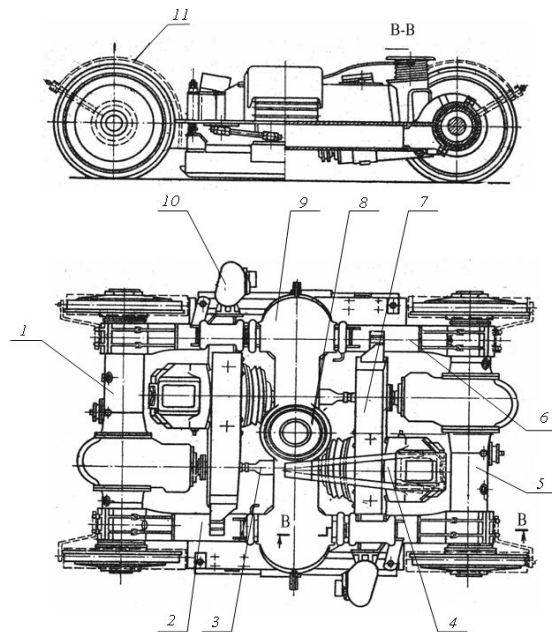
Візок вагона Т-3: 1, 5 – колісні пари, 2, 6 – поздовжні балки, 3 – карданний вал, 4 – тяговий двигун, 7 – балка для підвішування тягового двигуна, 8 – пятник, 9 – люлька візка, 10 – електромагнітний привід гальма, 11 – надколісні кожухи
